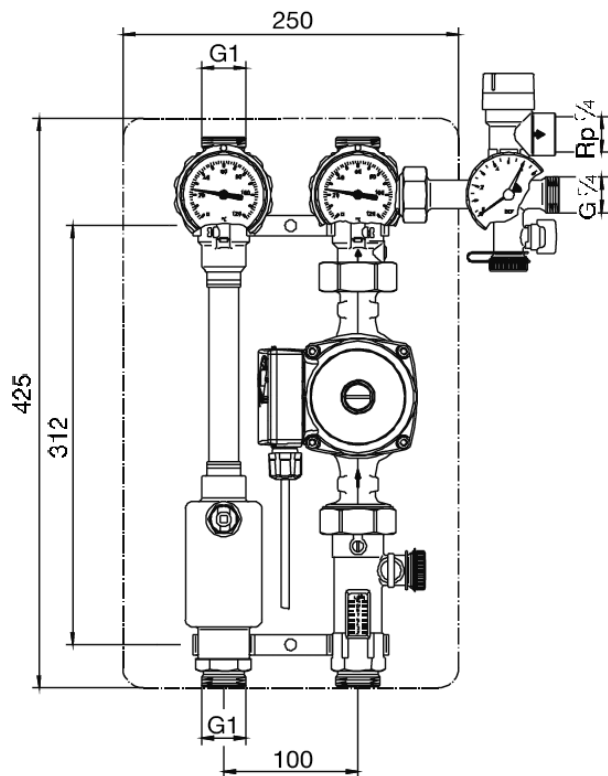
CIRCO 25/80 - Bemaßung in mm
